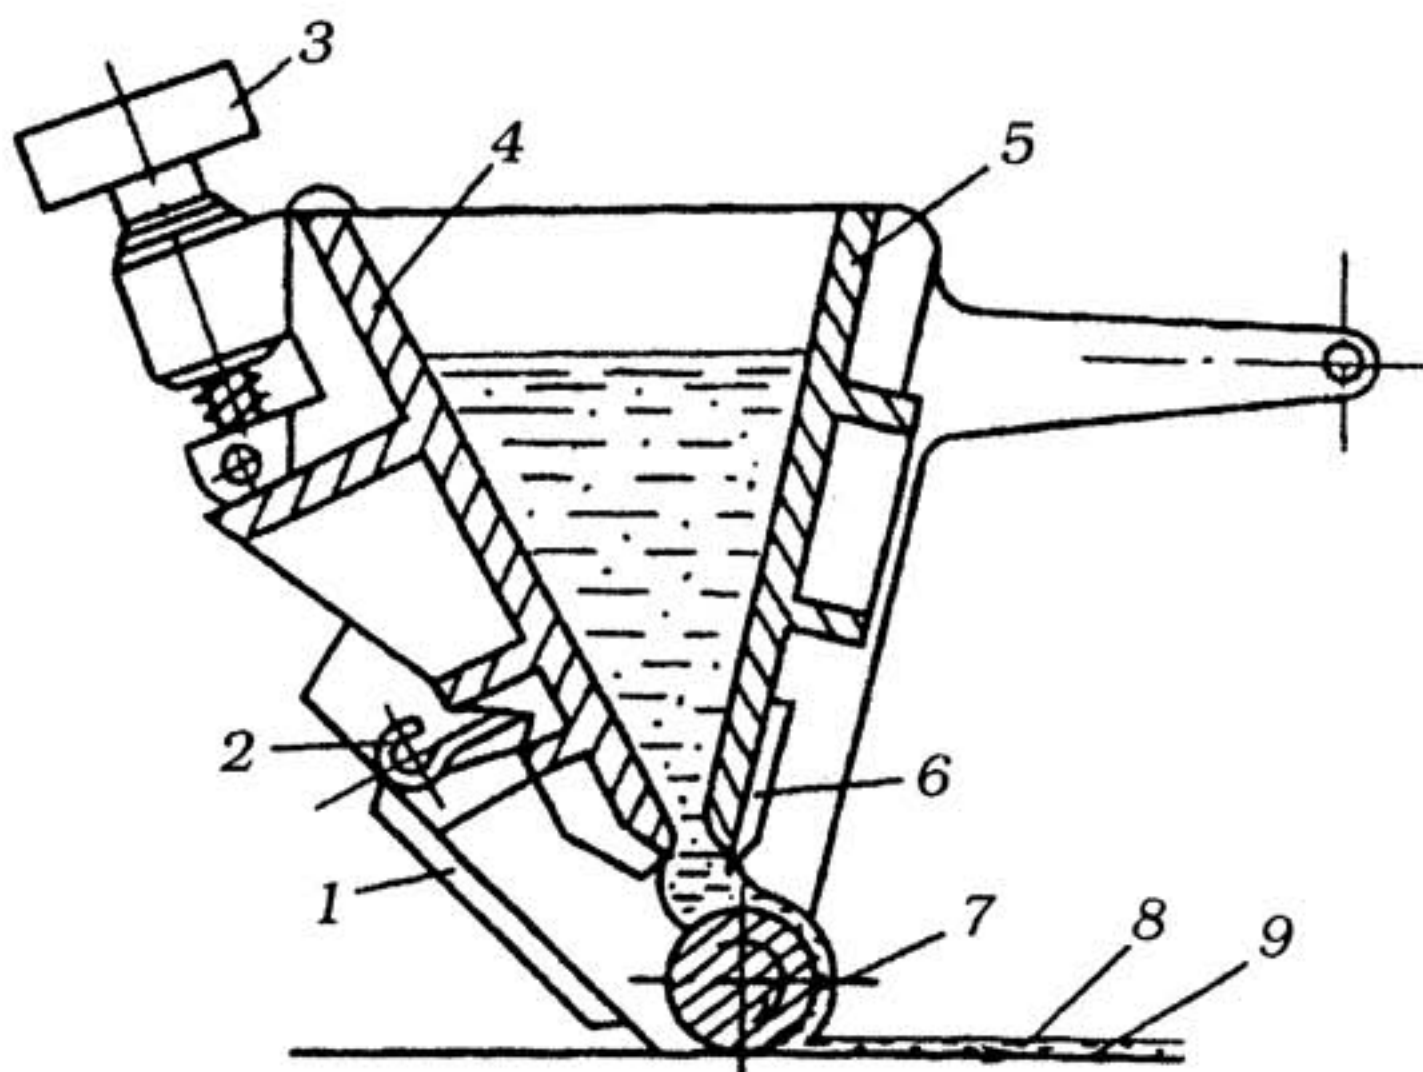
Фильера с валиком для отливки пленок из раствора:
